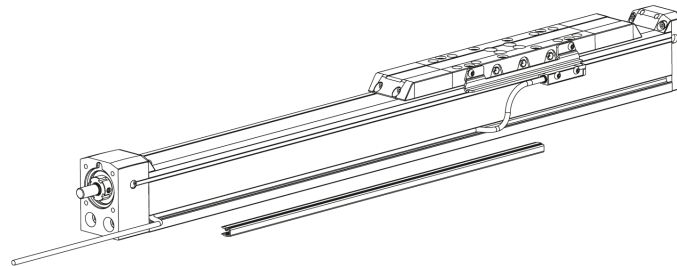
Montage du capteur fin de course : Placement des câbles
